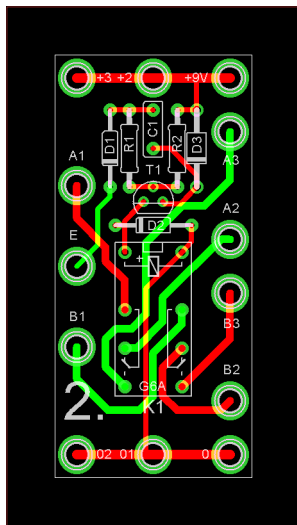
Nachbau 4: Doppelseitiges Layout für das Batteriegehäuse ([32263](#))
